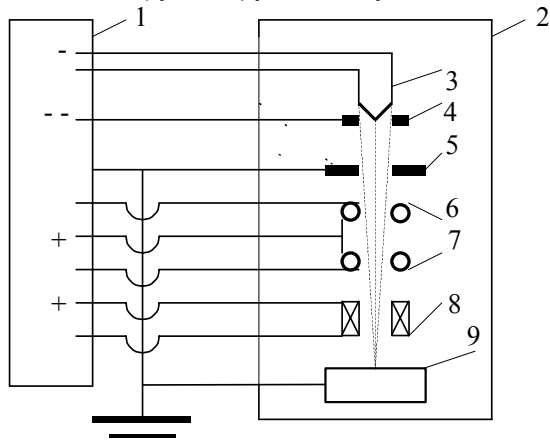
Общий вид устройства для электронно-лучевой сварки.
